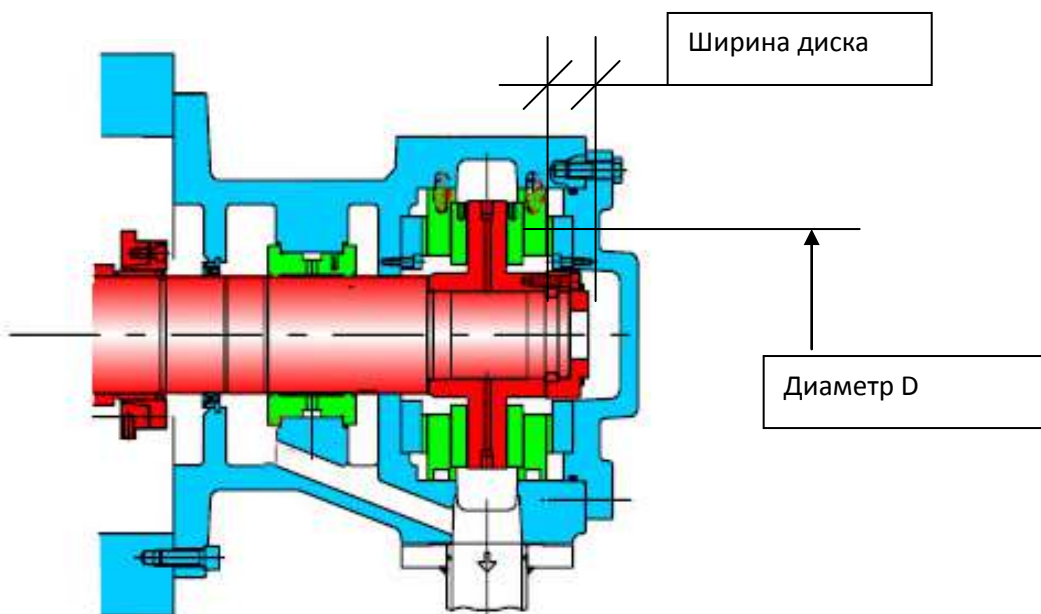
Внешний диаметр упорного подшипника 330 мм. Ширина упорного диска 50 мм.
